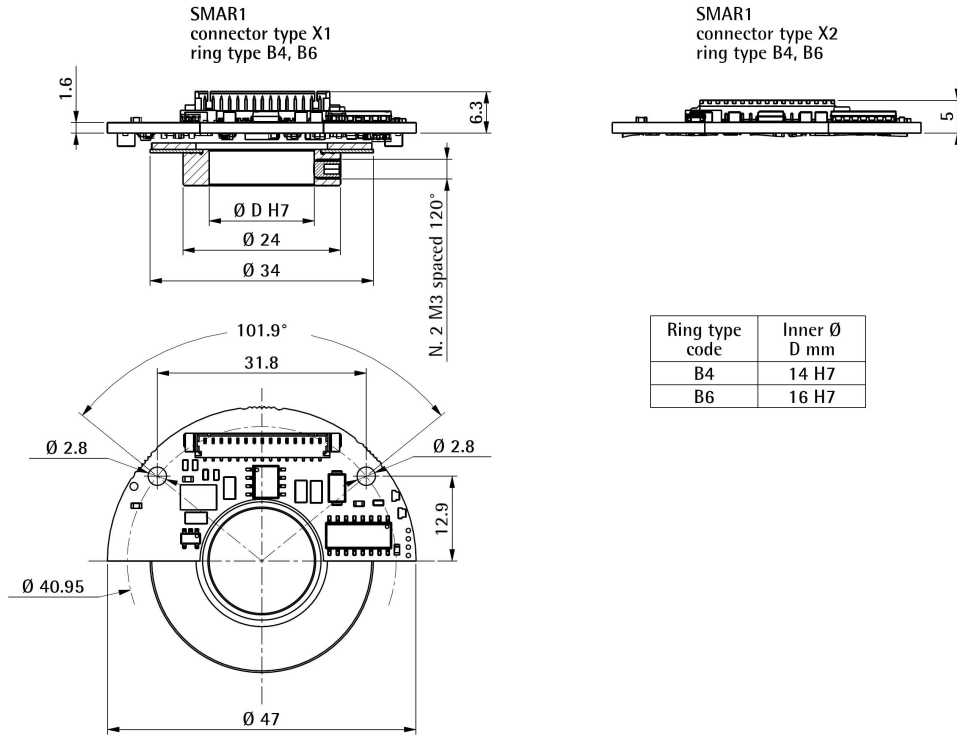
SMAR1 + MRA34B con supporto di montaggio meccanico
